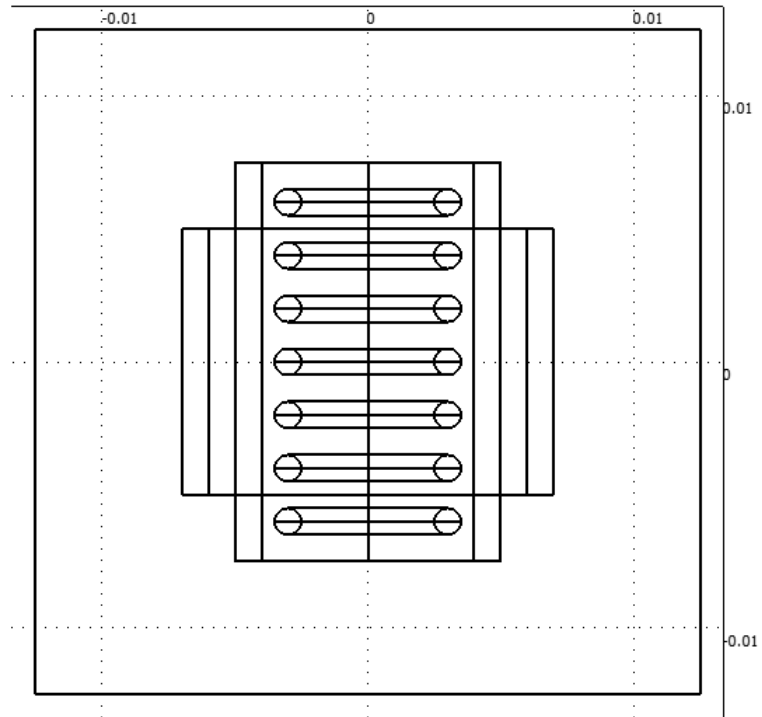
Le système d'assemblage des tubes par expansion 3D
